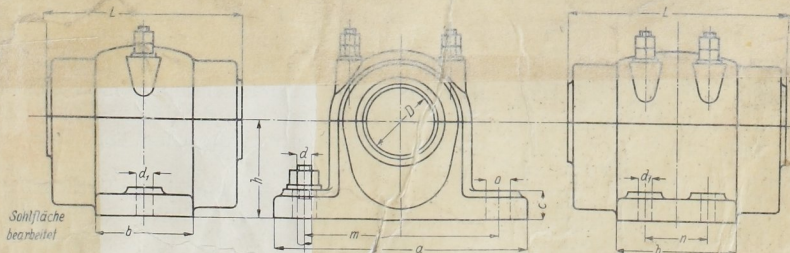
Stahllager nach DIN 118; links mit zwei, rechts mit vier Fußschrauben. Vgl. Zusammenstellung 133.
